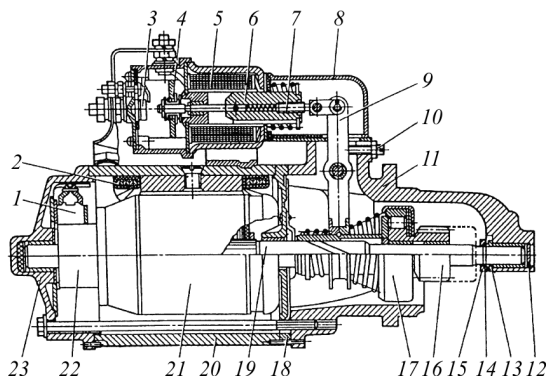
Стартер: 1 – щетка; 2 – обмотка возбуждения; 3, 4 – неподвижный и подвижный контакты тягового реле; 5 – обмотки тягового реле; 6 – якорь тягового реле; 7 – регулировочный винт; 8 – защитный кожух рычага; 9 – рычаг; 10 – винт регулировки хода шестерни; 11, 23 – крышки со стороны привода и коллектора; 12 – фиды; 13 – шайбы; 14, 15 – замковое и упорное кольца; 16 – шестерня привода; 17 – муфта свободного хода; 18 – промежуточная опора; 19 – вал якоря; 20 – корпус; 21 – якорь; 22 – коллектор
